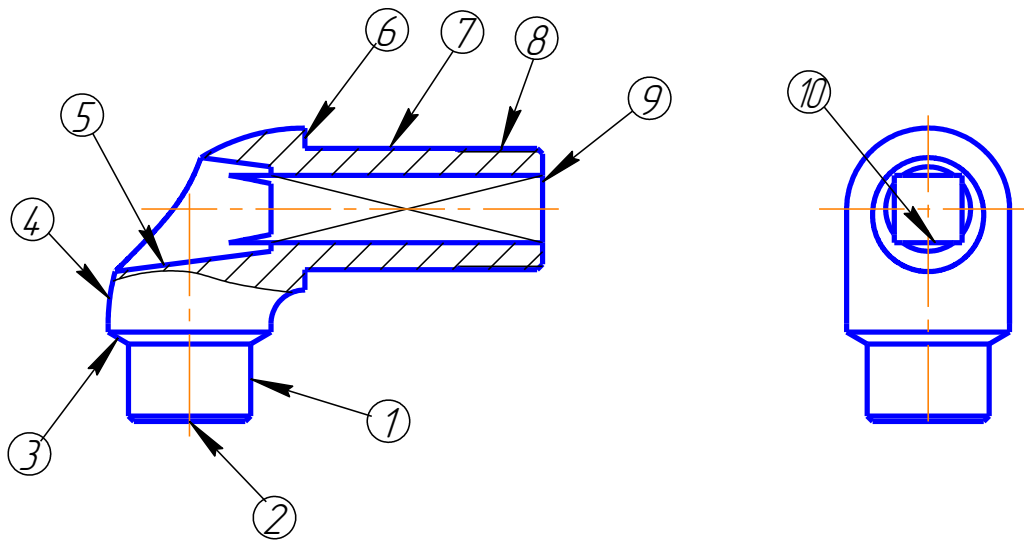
Конструкція та основні робочі поверхні деталі «Цапфа ричага».
